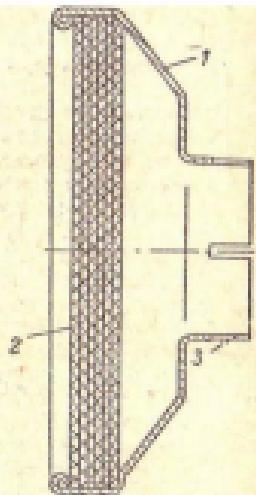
Воздухоочиститель двигателя мотороллера „Тула“:
